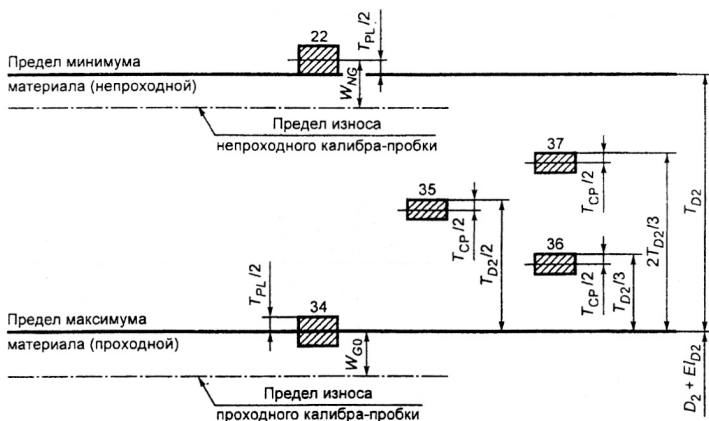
Схемы расположения полей допусков среднего диаметра калибров для контроля внутренней резьбы по ГОСТ 4608 с сортировкой на группы
